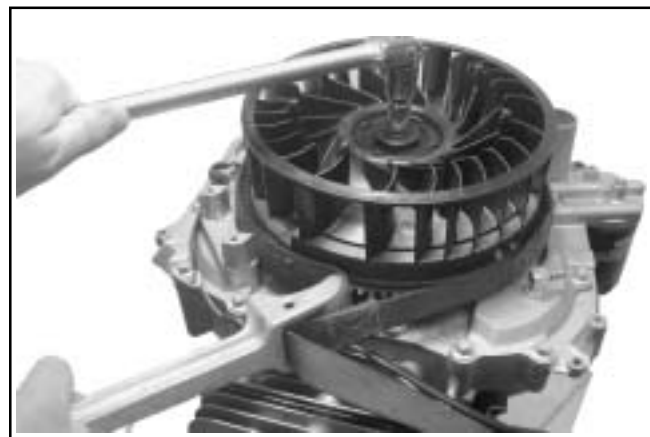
Desmontaje del ventilador y los accesorios de montaje del volante del motor
